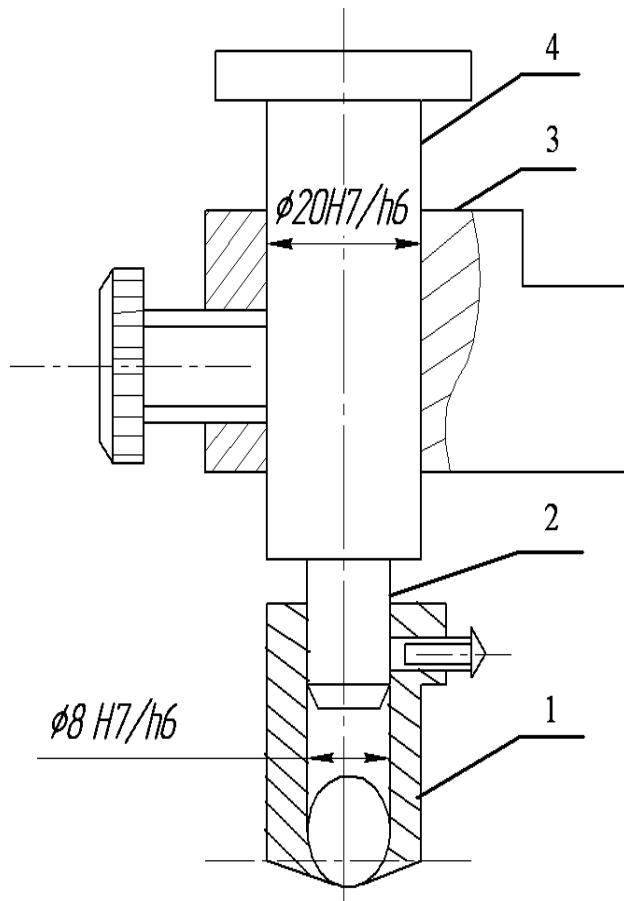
Посадка сменного наконечника 1 на штифт 2 стержня прибора; посадка стержня прибора 4 в корпусе 3
